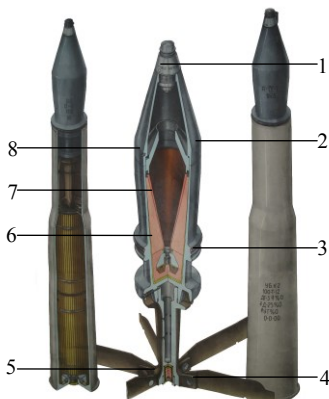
Необертальний оперений кумулятивний снаряд: 1 – головний підривник; 2 – корпус; 3 – плаваюче кільце з ведучим пояском; 4 – стабілізувальний пристрій; 5 – трасер; 6 – розривний заряд; 7 – облицювання кумулятивної воронки; 8 – пригвинтна головка
